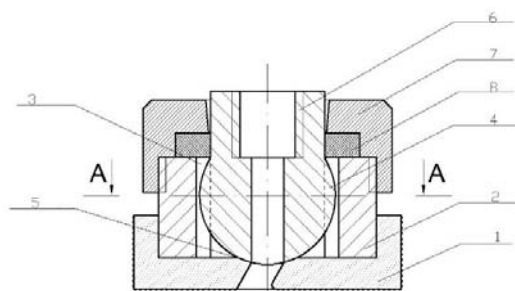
Долото с шарнирным соединением для отклонителей фрезерующего типа.
